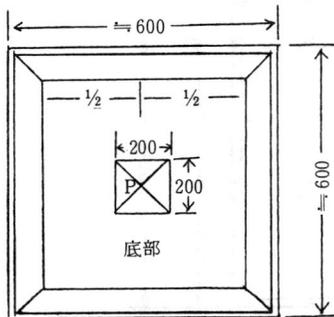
収納庫 (シェル) 静荷重試験方法 (平面図)
